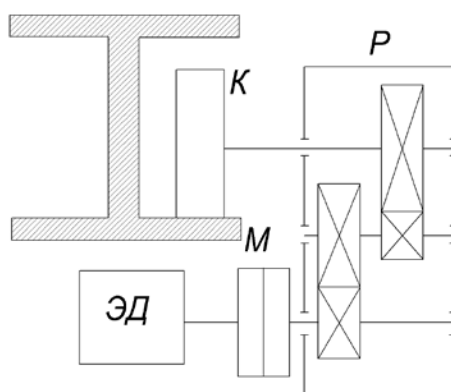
Кинематическая схема привода «мотор-редуктор-колесо»
